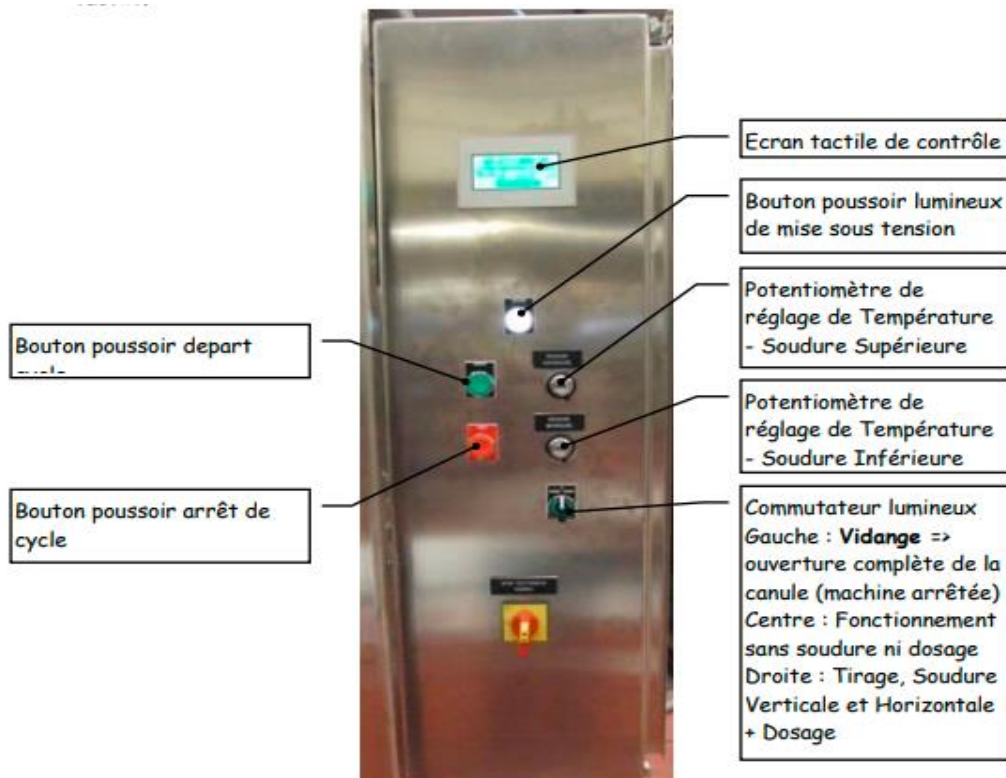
Photo réelle d'unité de commande de la machine.
